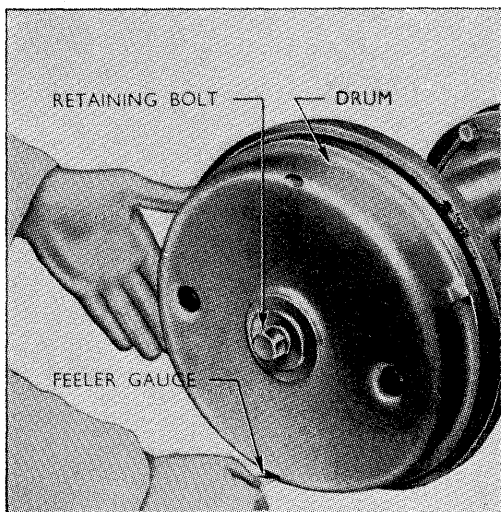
Afprøvning af bremsebakkerens centre-ring med Feeler gauge = søgerblad.
